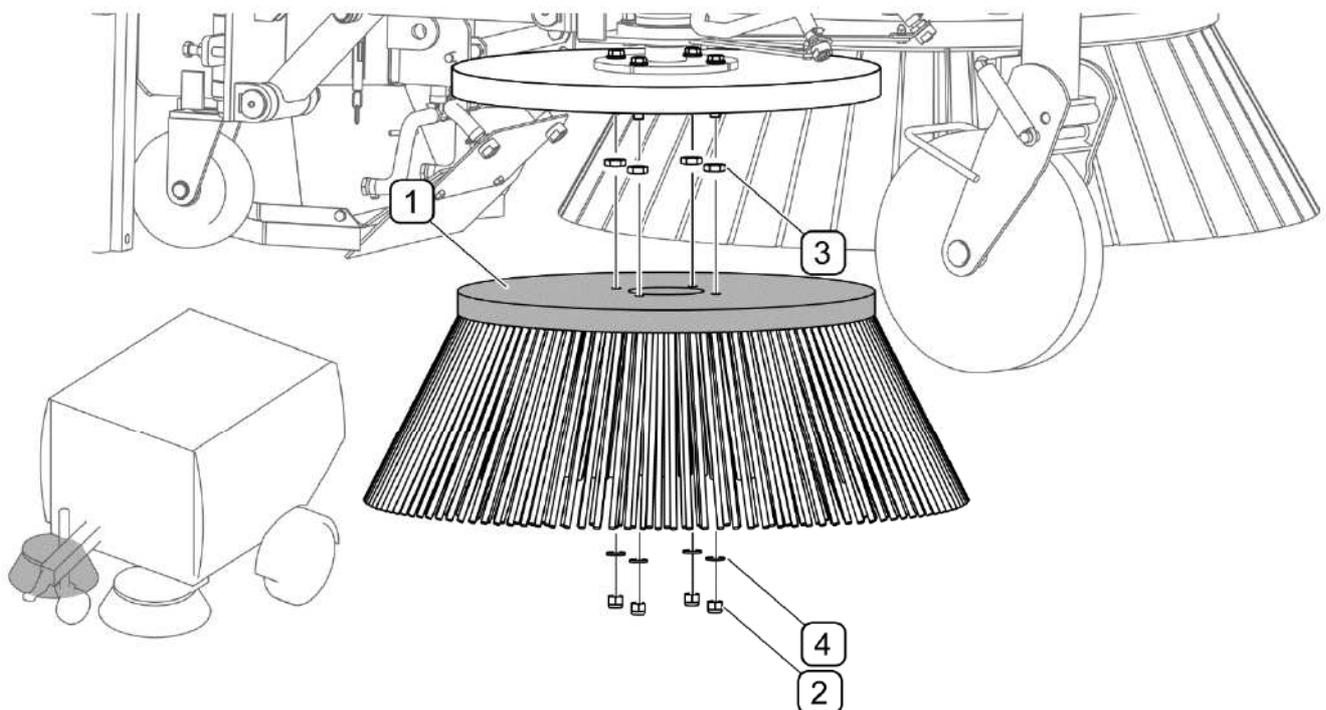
Le remplacement de la brosse à disque I (droite)
